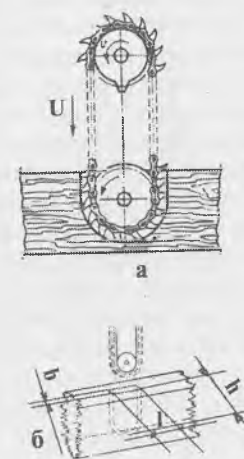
Схема выборки гнезд фрезерной цепочкой (а), размеры гнезд (б)
